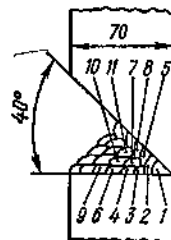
Порядок наложения швов при сварке горизонтального шва.
